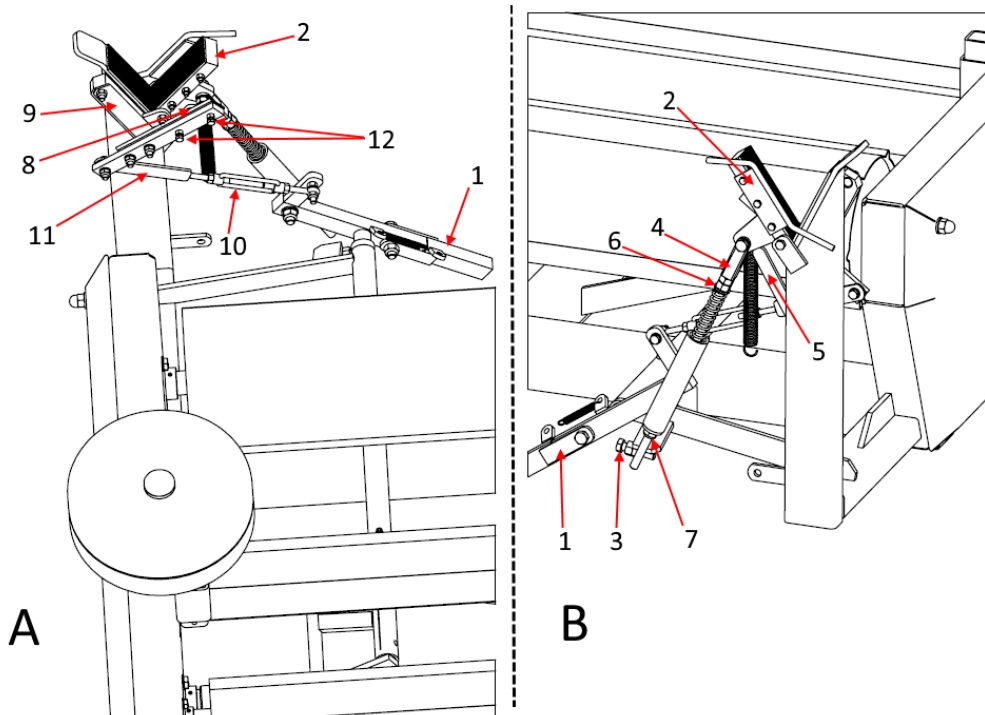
Coupe-film ouvert : A – vue arrière, B – vue avant
